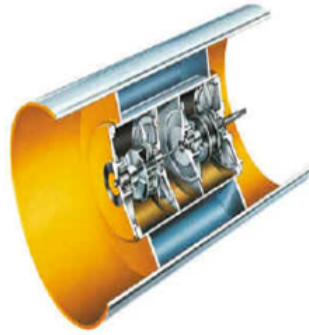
Excéntricas de tambor de rodillo vibratorio
